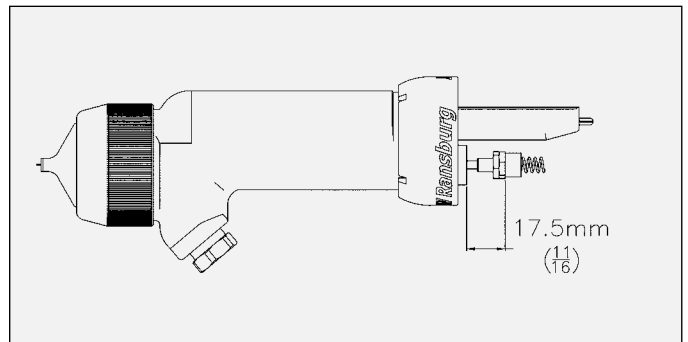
Dimensiones de tuerca de ajuste del gatillo
